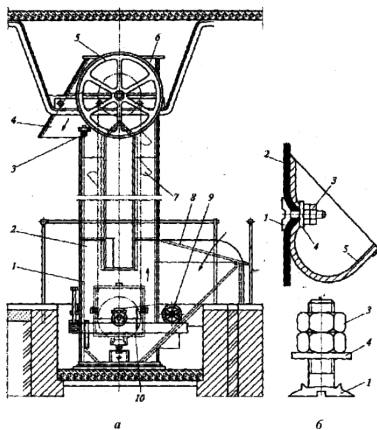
Ковшовый элеватор (нория): а — общий вид элеватора; б — крепление ковша. Ковшовый ленточный элеватор состоит из двух барабанов — приводного 5 и ведомого (натяжного) 10, на которые натягивается бесконечная лента с укрепленными на ней металлическими ковшами 7.
